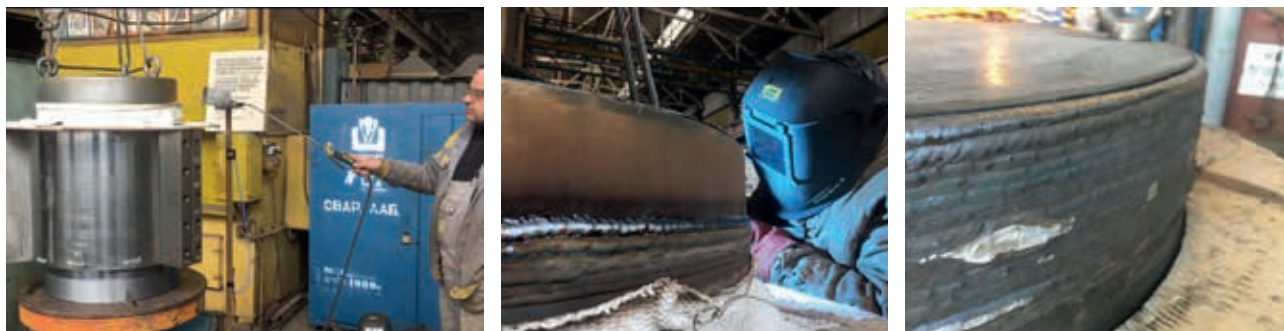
Наплавка поверхностей МИГ/МАГ сваркой
